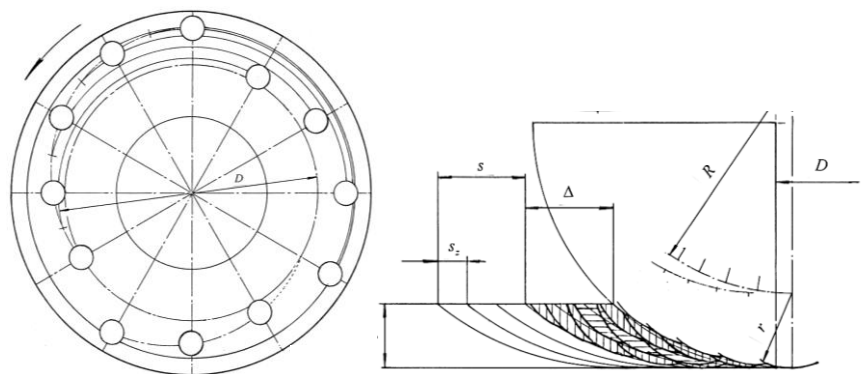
Розташування ножів і схема різання ножами типу «риб'яча луска» для ТФ
